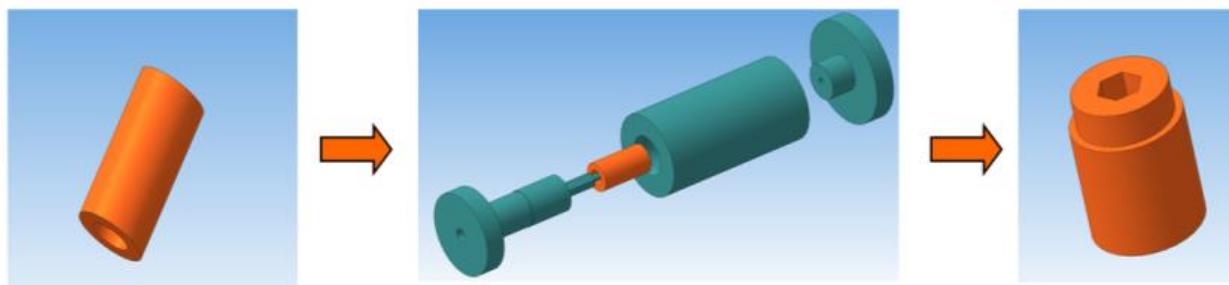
3D-модель процесса изготовления опорного изолятора
